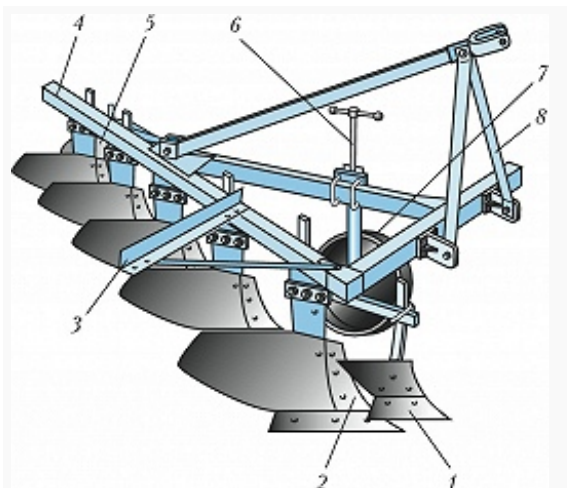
Плуг лемешный навесной пятикорпусный: 1 – предплужник; 2 – корпус; 3 – прицеп для борон; 4 – рама; 5 – дисковый нож; 6 – регулятор глубины вспашки; 7 –...
